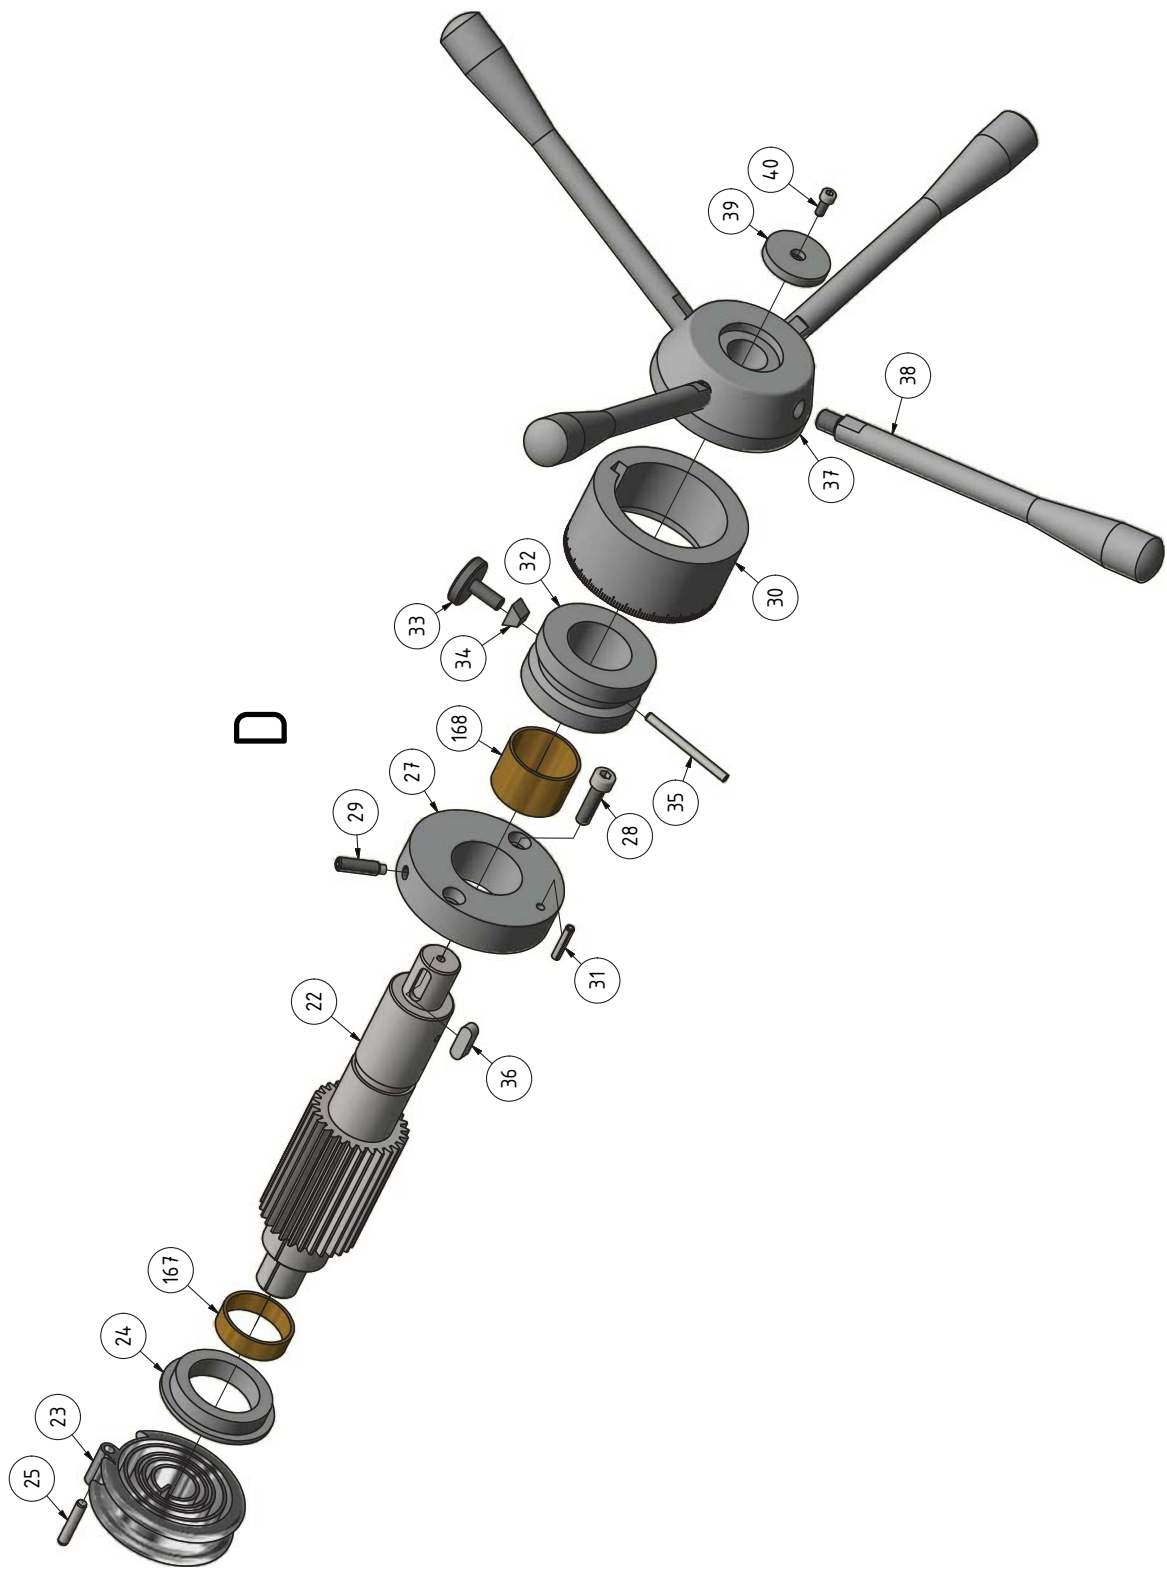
Bohrkopf 3 von 5 - Drilling head 3 of 5
